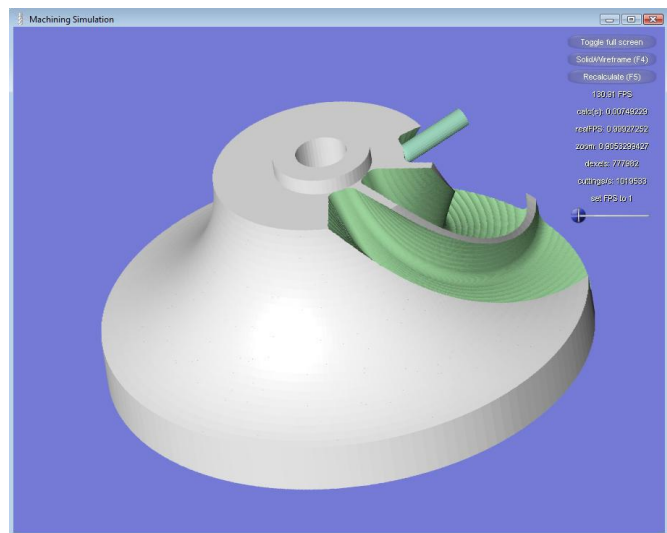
Моделювання видалення матеріалу під час фрезерування заготовки [15]
